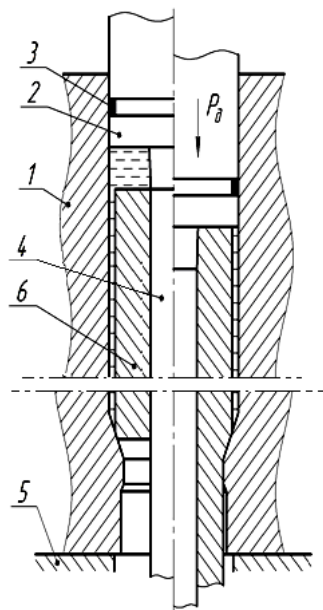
Схема гидропрессования трубчатых заготовок на оправке
